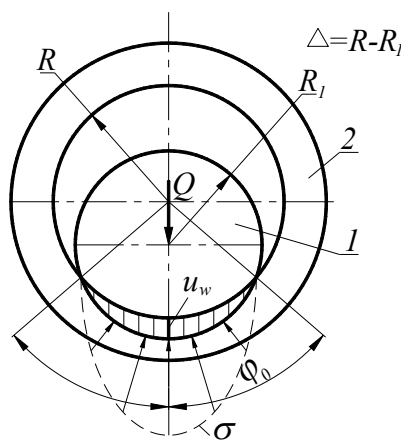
Розрахункова схема циліндричного підшипника ковзання
